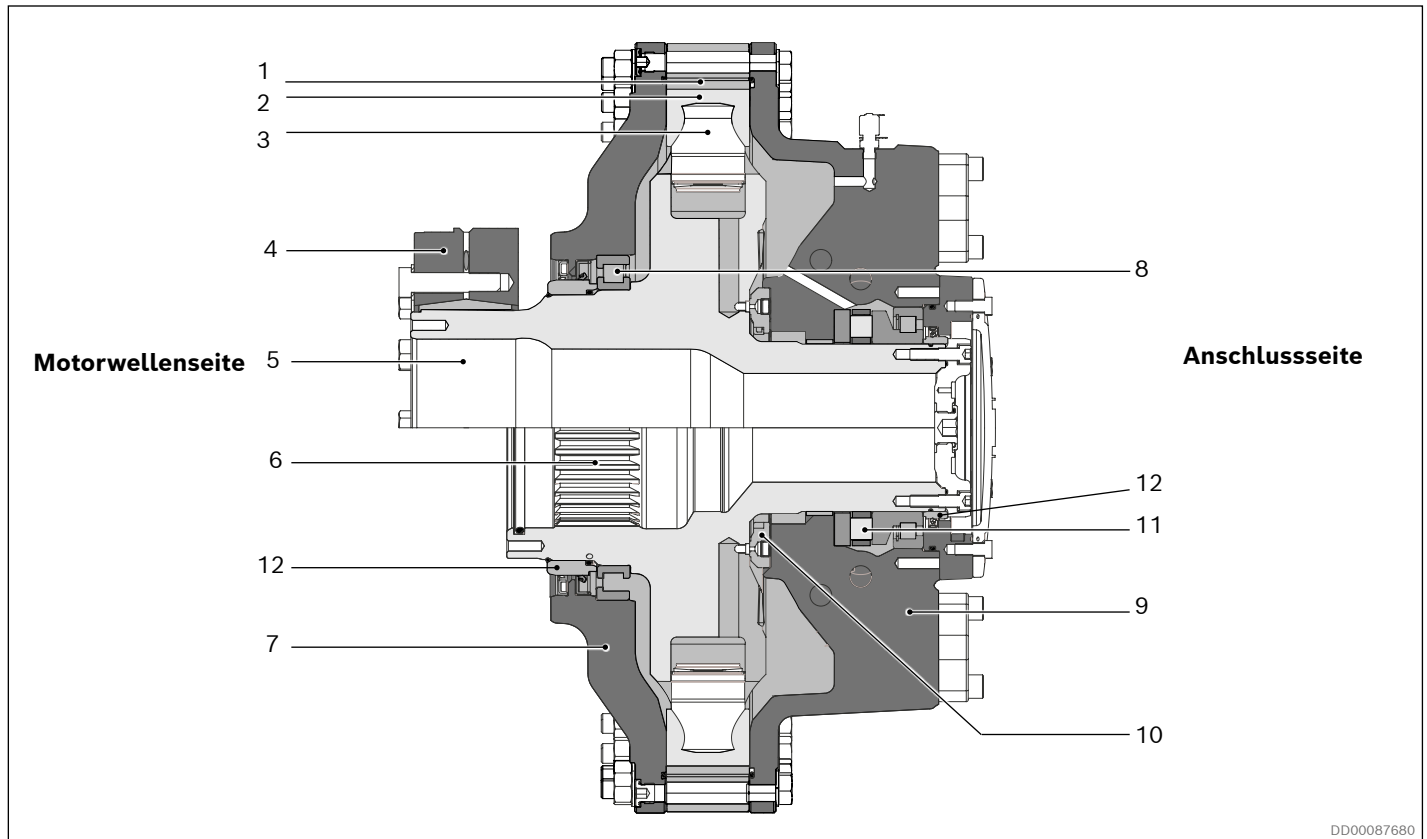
Querschnittansicht von Radialkolben-Hydraulikmotor
